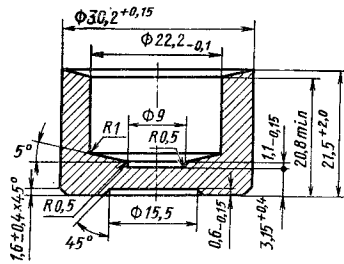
Штампованная заготовка корпуса карданного подшипника
